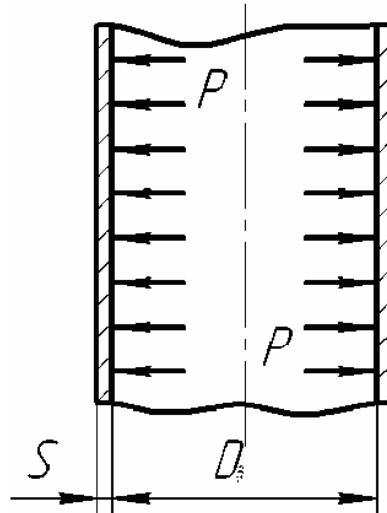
Розрахункова схема циліндричної обичайки
